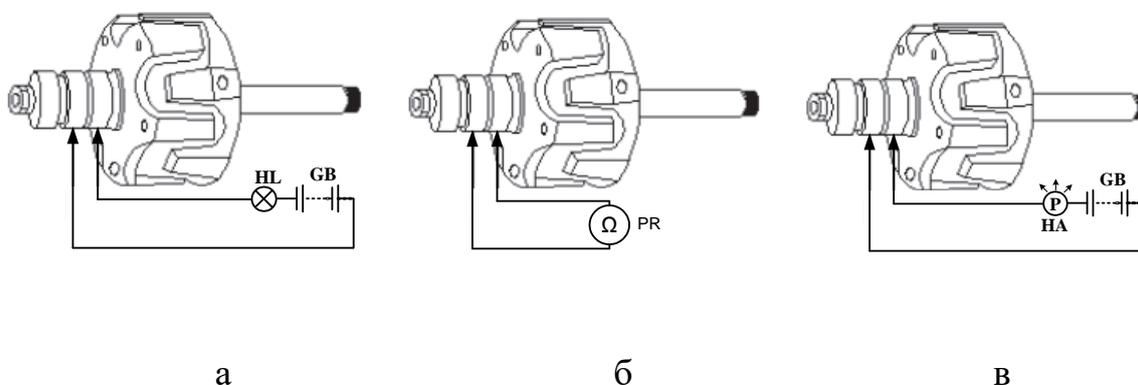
Схема проверки обмотки возбуждения на обрыв
